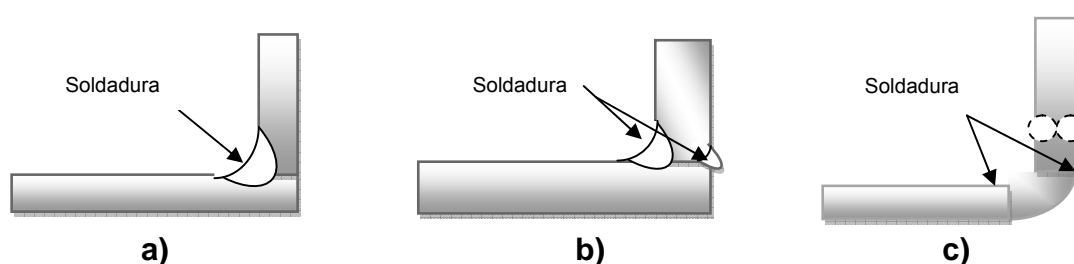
a) Esquina soldada desde el interior del tanque (diseño pobre por dentro); b) Esquina soldada desde ambos lados (Diseño pobre en el interior pero mejor diseño por fuera del tanque); c) Soldadura en la pared de la esquina con un mejor diseño en el interior y afuera del tanque el cual tiene buena resistencia a la corrosión y a la fatiga. ^[15]
